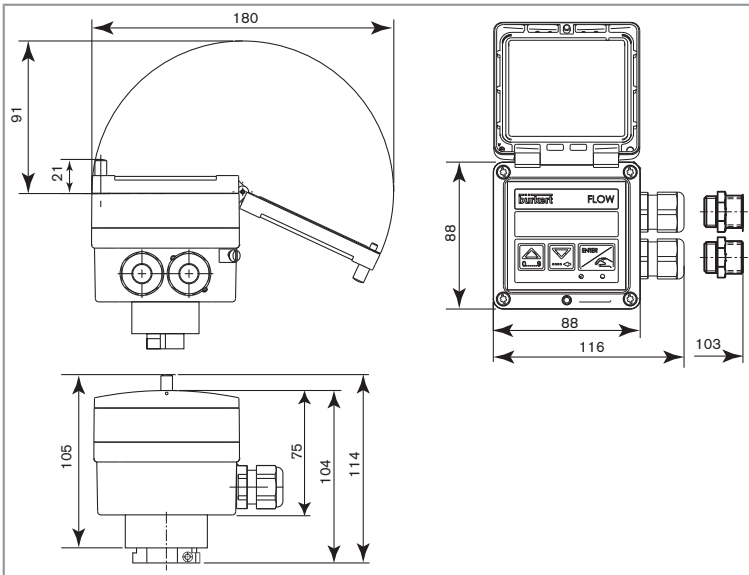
Dimensions du module électronique SE35 du transmetteur de débit 8035
